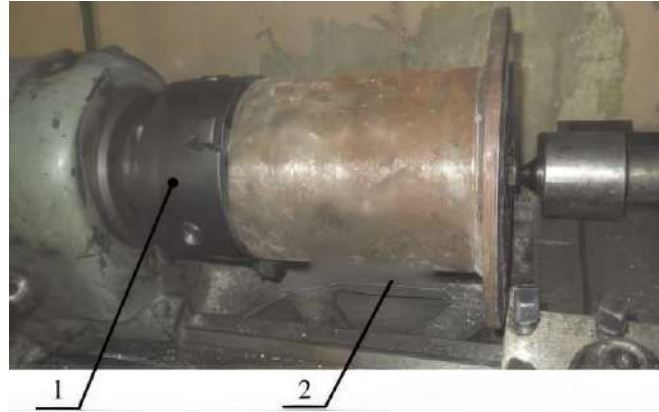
Оснащення для зміцнення конічних шестерень на токарному верстаті шляхом динамічного наклепу поверхонь зубів сталевими кульками та порошком фторованого графіту: 1 - патрон токарного верстата; 2 – робоча ємність
